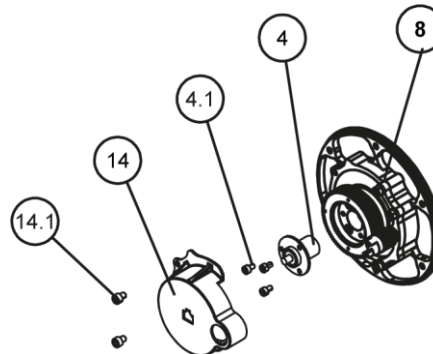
Explosionszeichnung Passive flange tilt mit Gear cover tilt und Slip ring tilt
